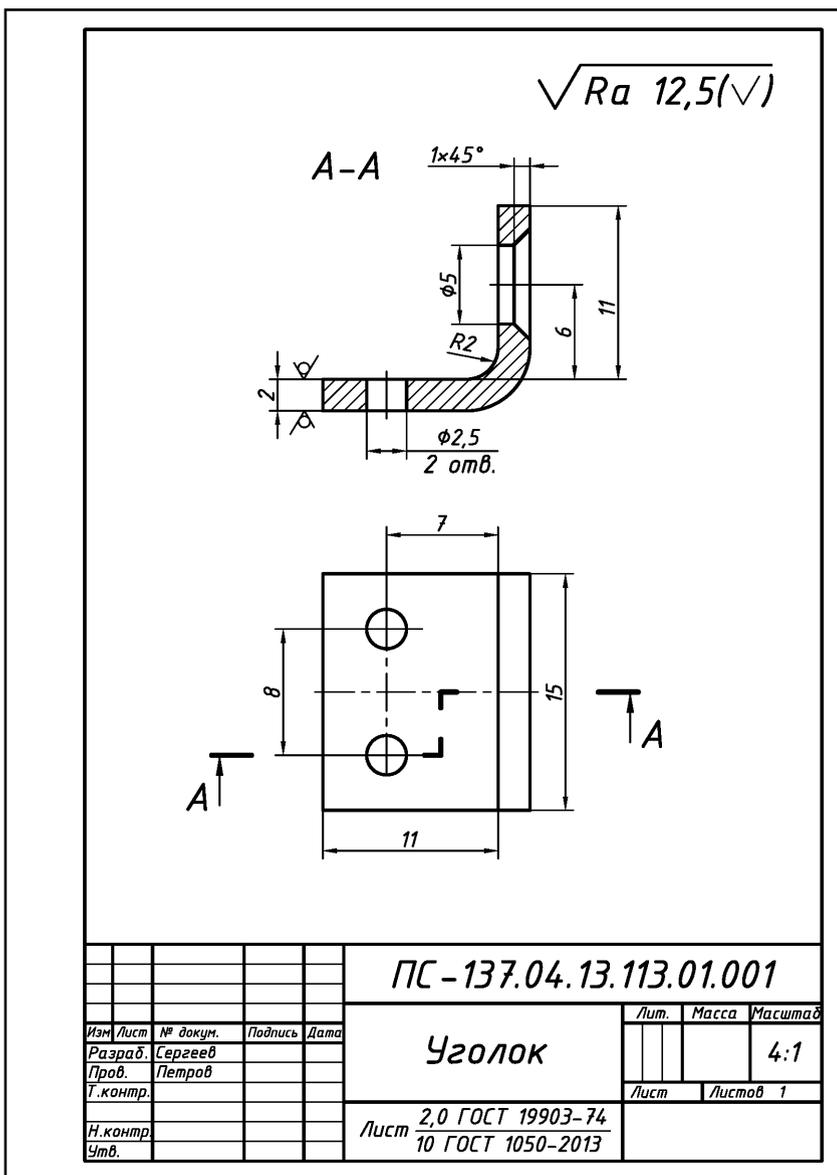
Оформление рабочего чертежа детали «Уголок»
